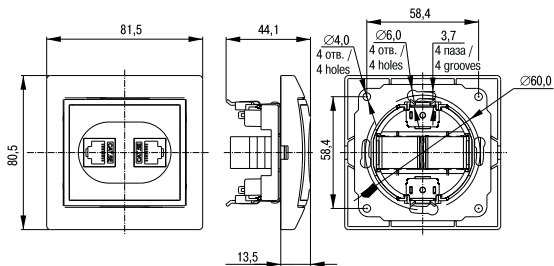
Габаритные и присоединительные размеры PK12-КБ, PK12-ККм /
